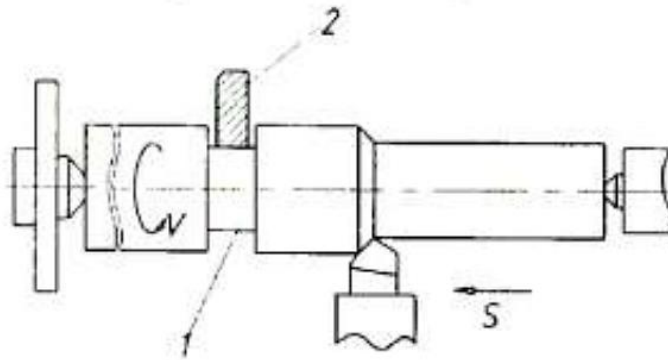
Схема обробки валу за допомогою нерухомого люнету
